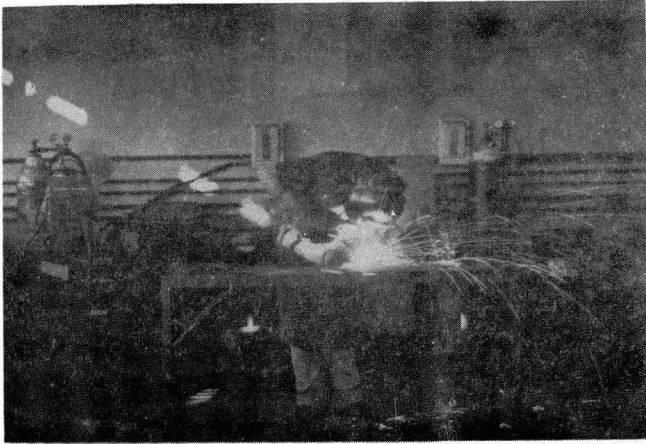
Equipamento para Soldagem: SAER, SATG, SAMG
